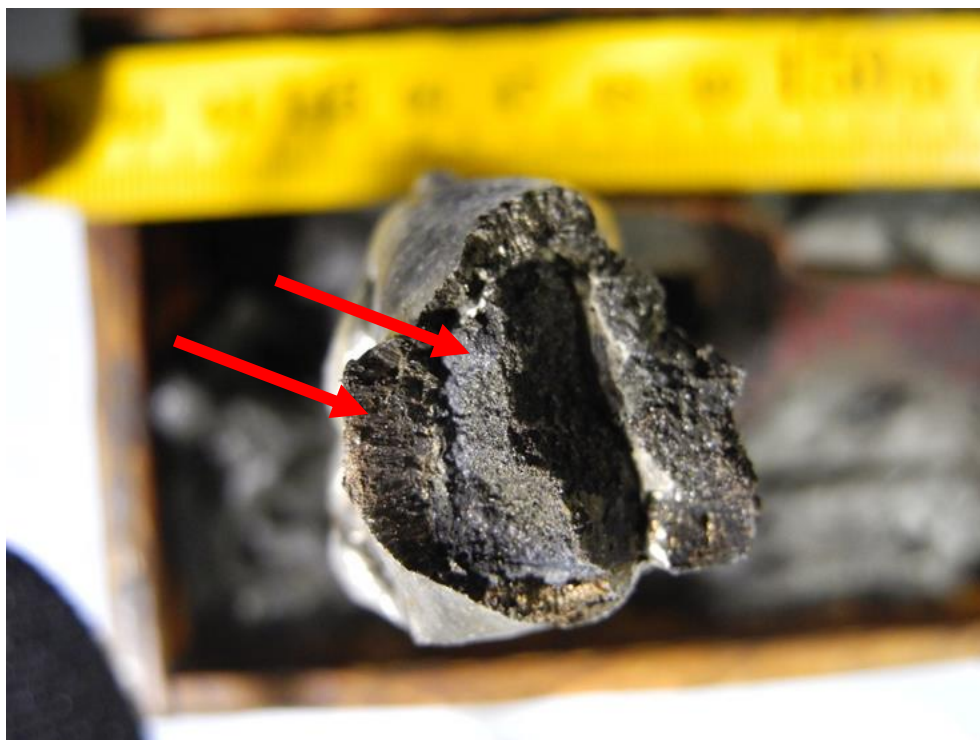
Bruchfläche – Mitte Grundwerkstoff; Rand – „Mantel“ aus Schweißgut
